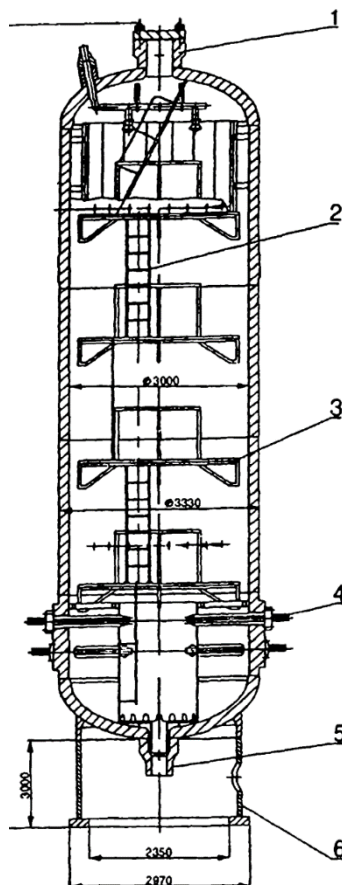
КД ВВЭР-1000: 1 – горловина; 2 – лестница; 3 – площадка; 4 – блок трубчатых электронагревателей; 5 – патрубок; 6 – опора
